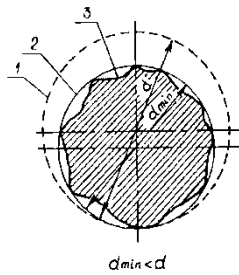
Прилегле коло для зовнішніх поверхонь обертання
